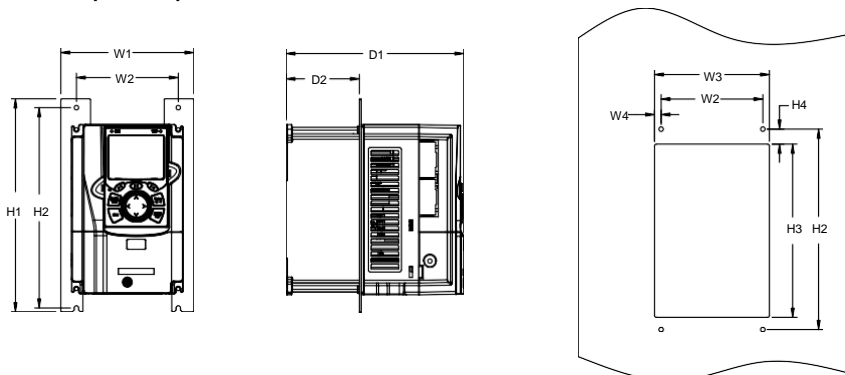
Схема фланцевого монтажа ПЧ напряжением 380 В, от 1,5 до 75 кВт
